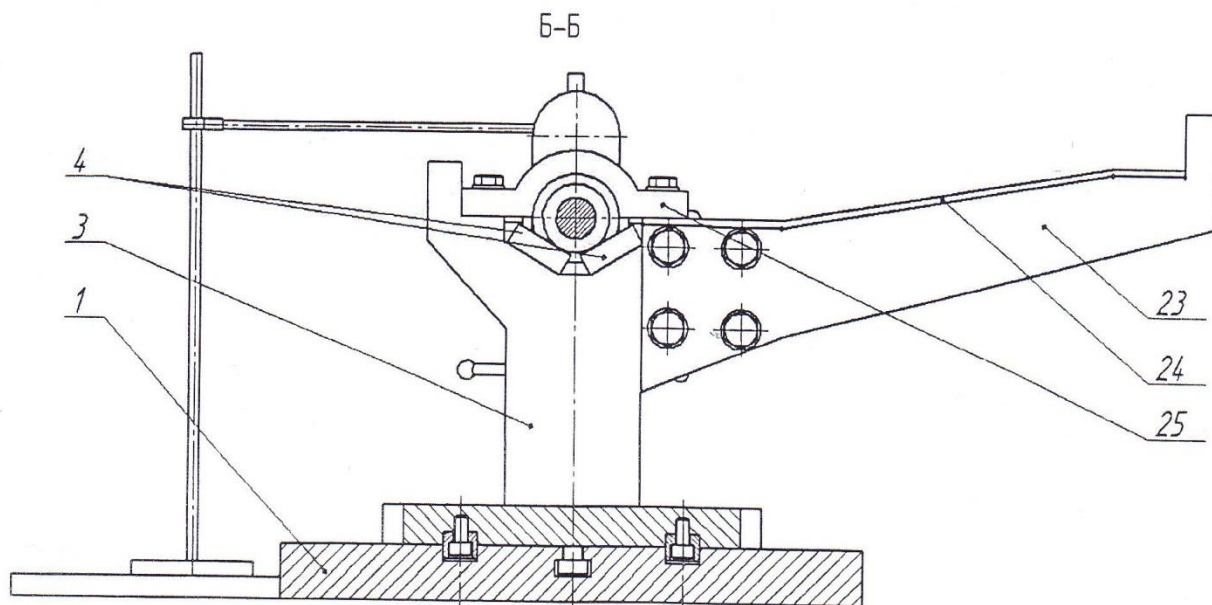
Новое устройство для проверки изгиба коленчатого вала на центрах и выпрямления на гидравлическом прессе, вид сечения Б-Б
